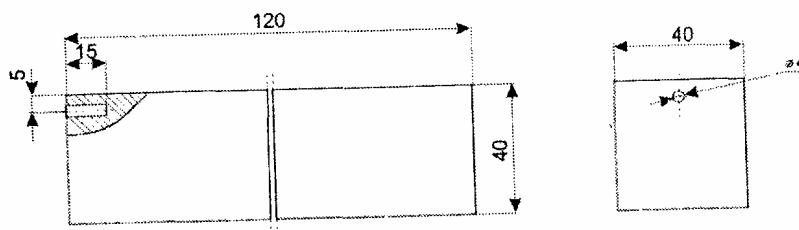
Стандартный образец предприятия для контроля сварных соединений главными волнами.
